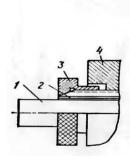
Устройство цангового стопора: 1-микровинт; 2 – разрезная гильза; 3 – гайка; 4 – скоба
